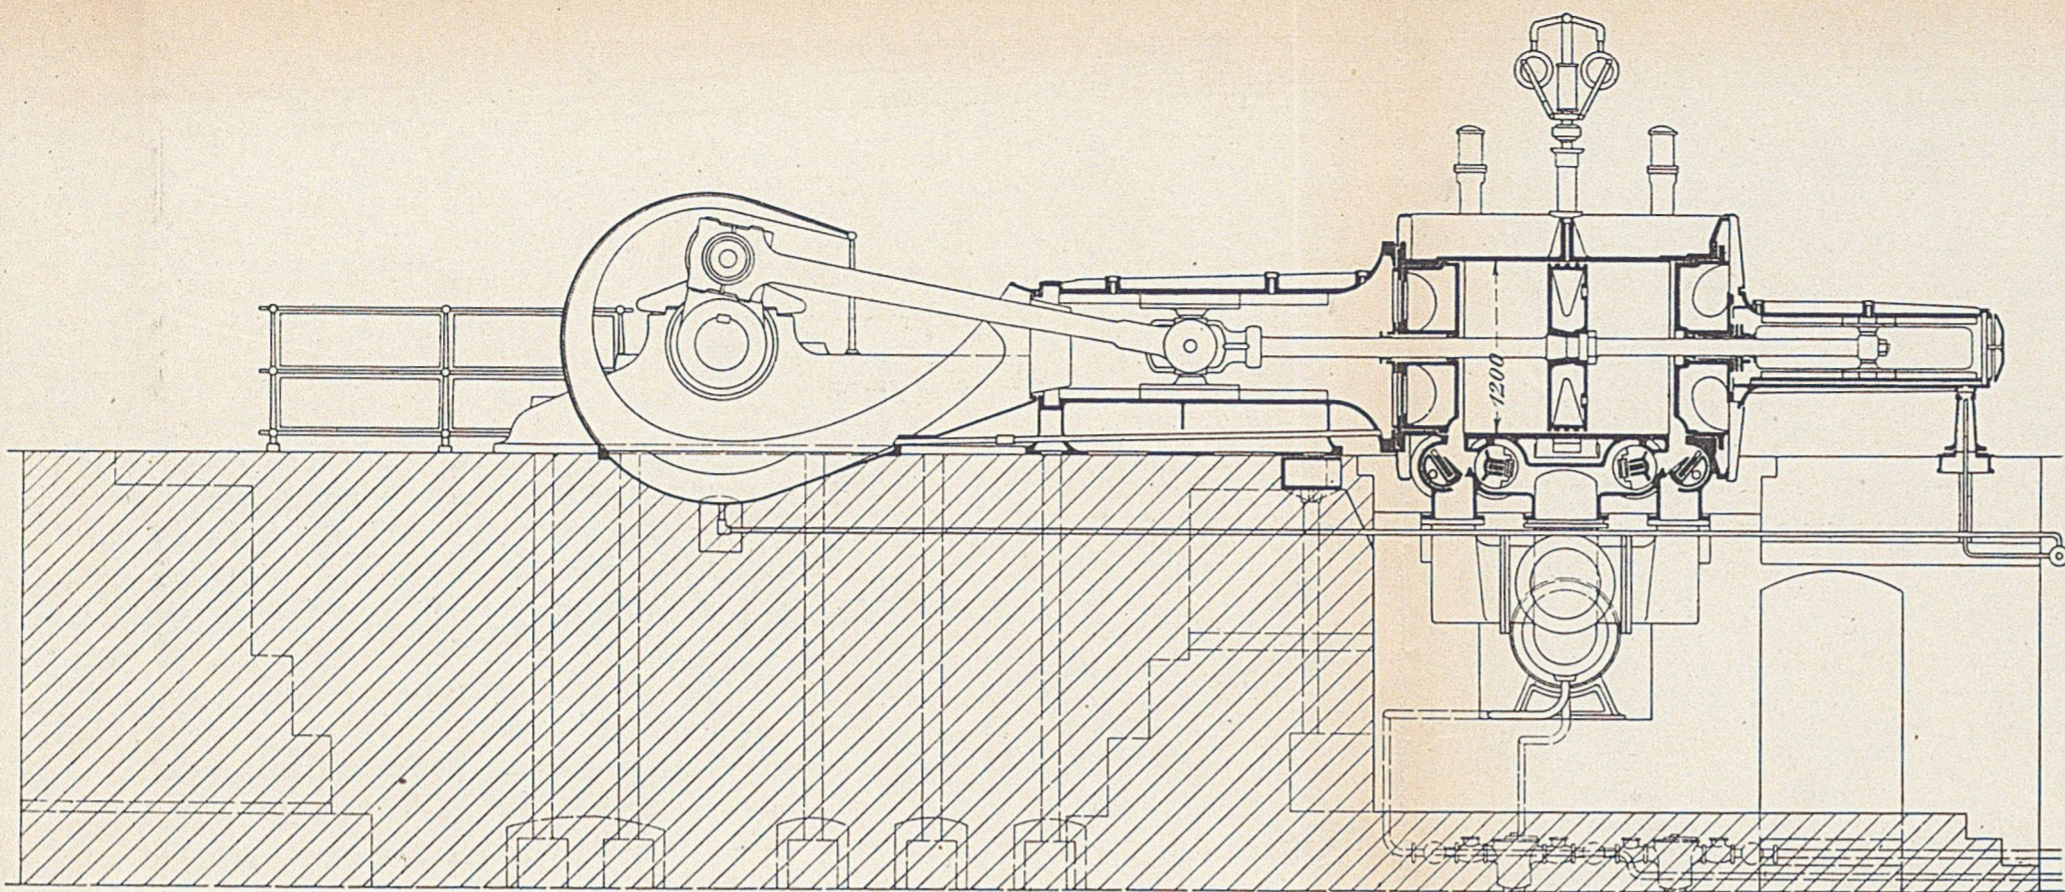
Längsschnitt durch den Niederdruckzylinder.
